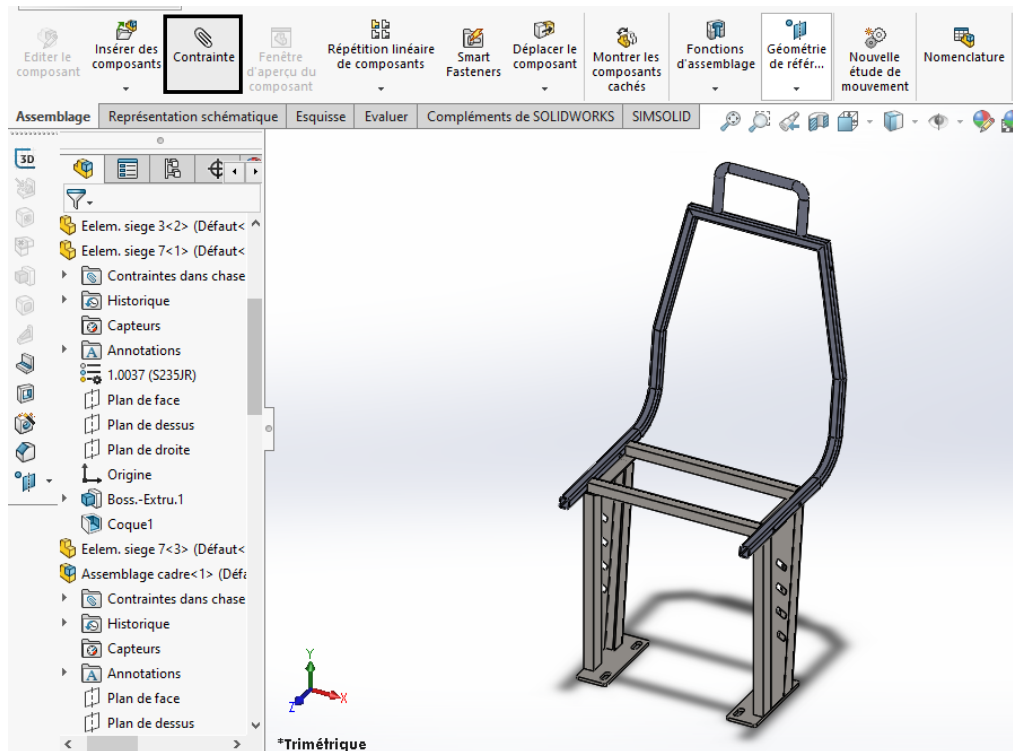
Le châssis de la chaise a été assemblé sur SolidWorks 2017.
